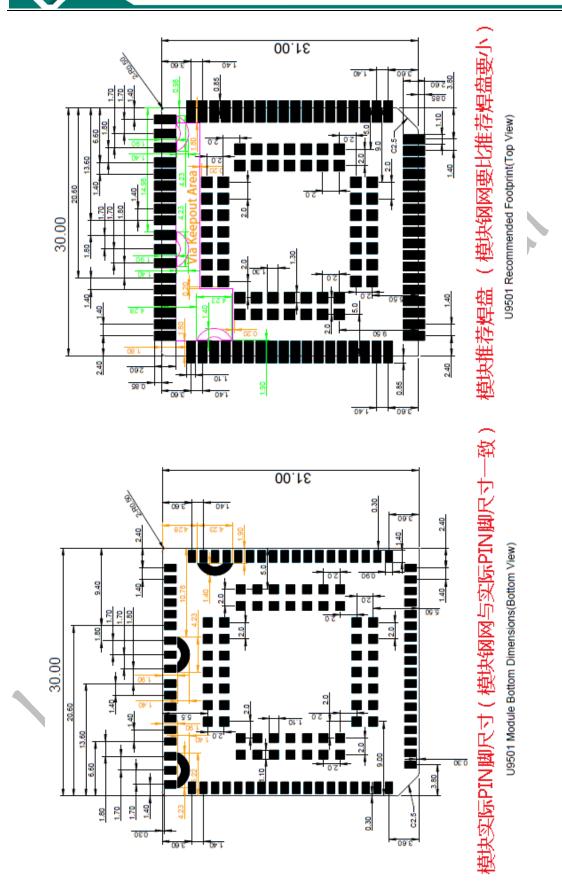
U9501 模块实际 PIN 尺寸与推荐焊盘尺寸
